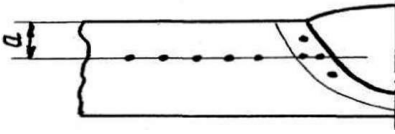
Схема розташування зон випробування при вимірюванні твердості зварного з'єднання
